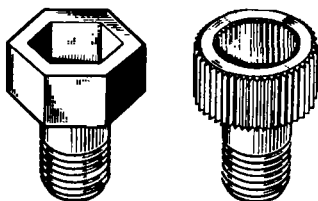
Головки болтов с внутренними и наружными свертными элементами
